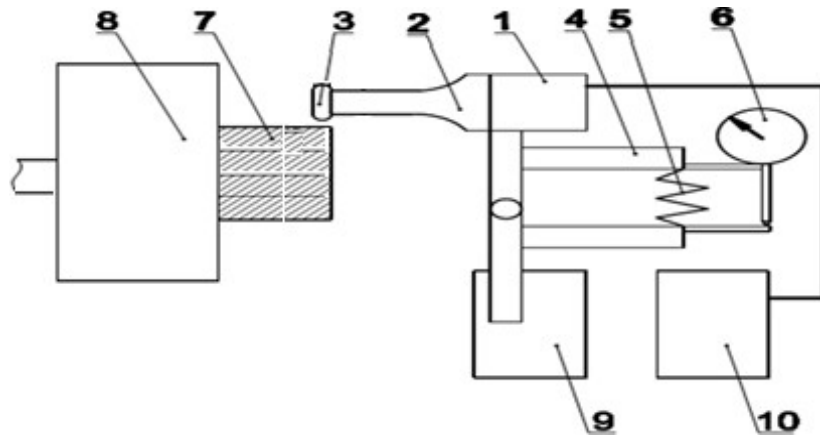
Схема стенду для ультразвукової обробки металу:
